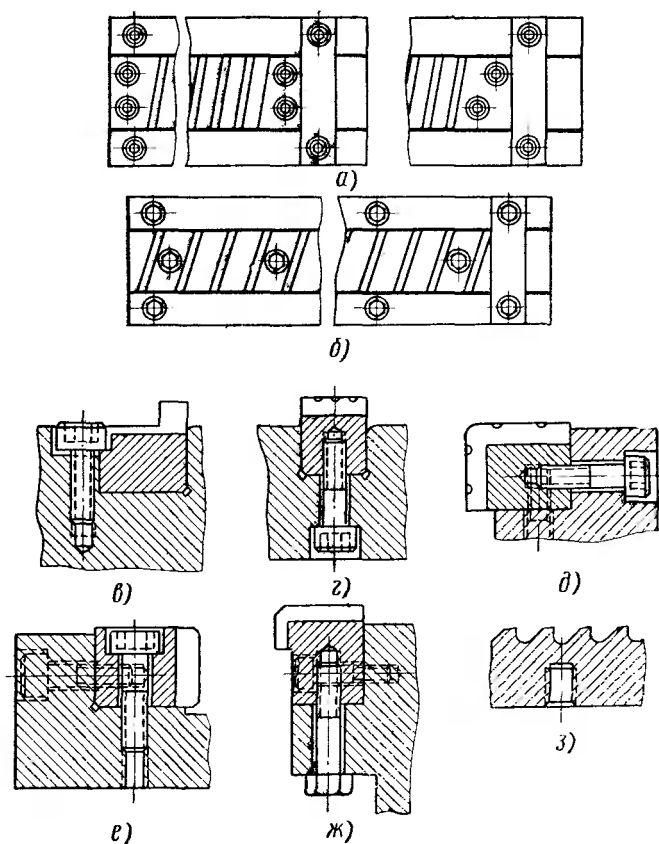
Крепление к корпусу секций рабочей части наружных протяжек
